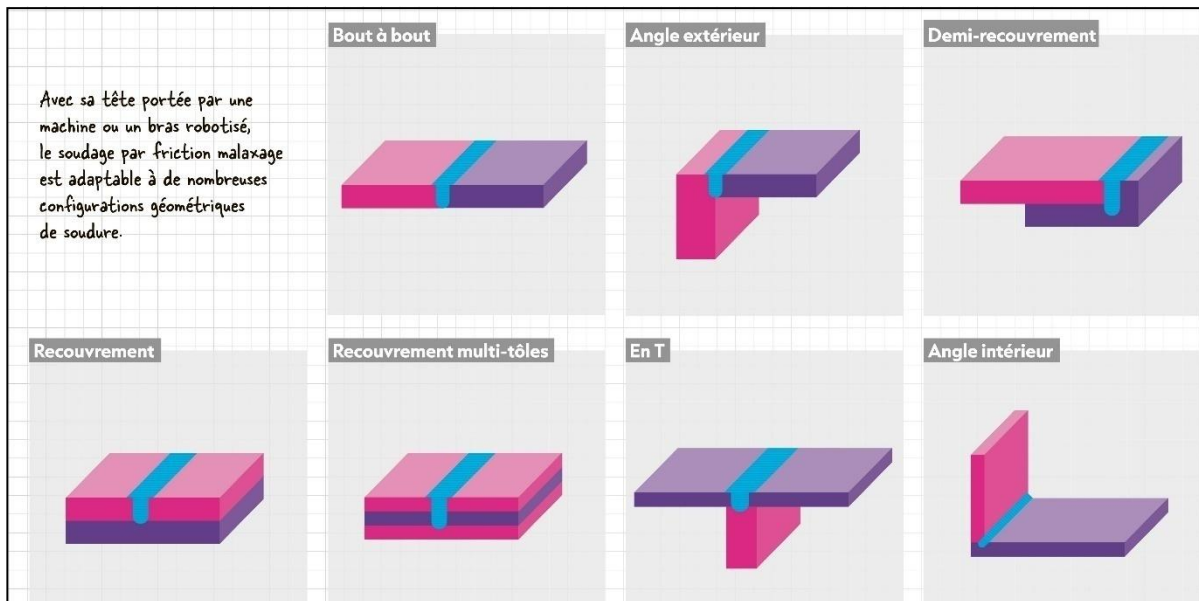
Les formes des joints de soudure FSW. [14]
